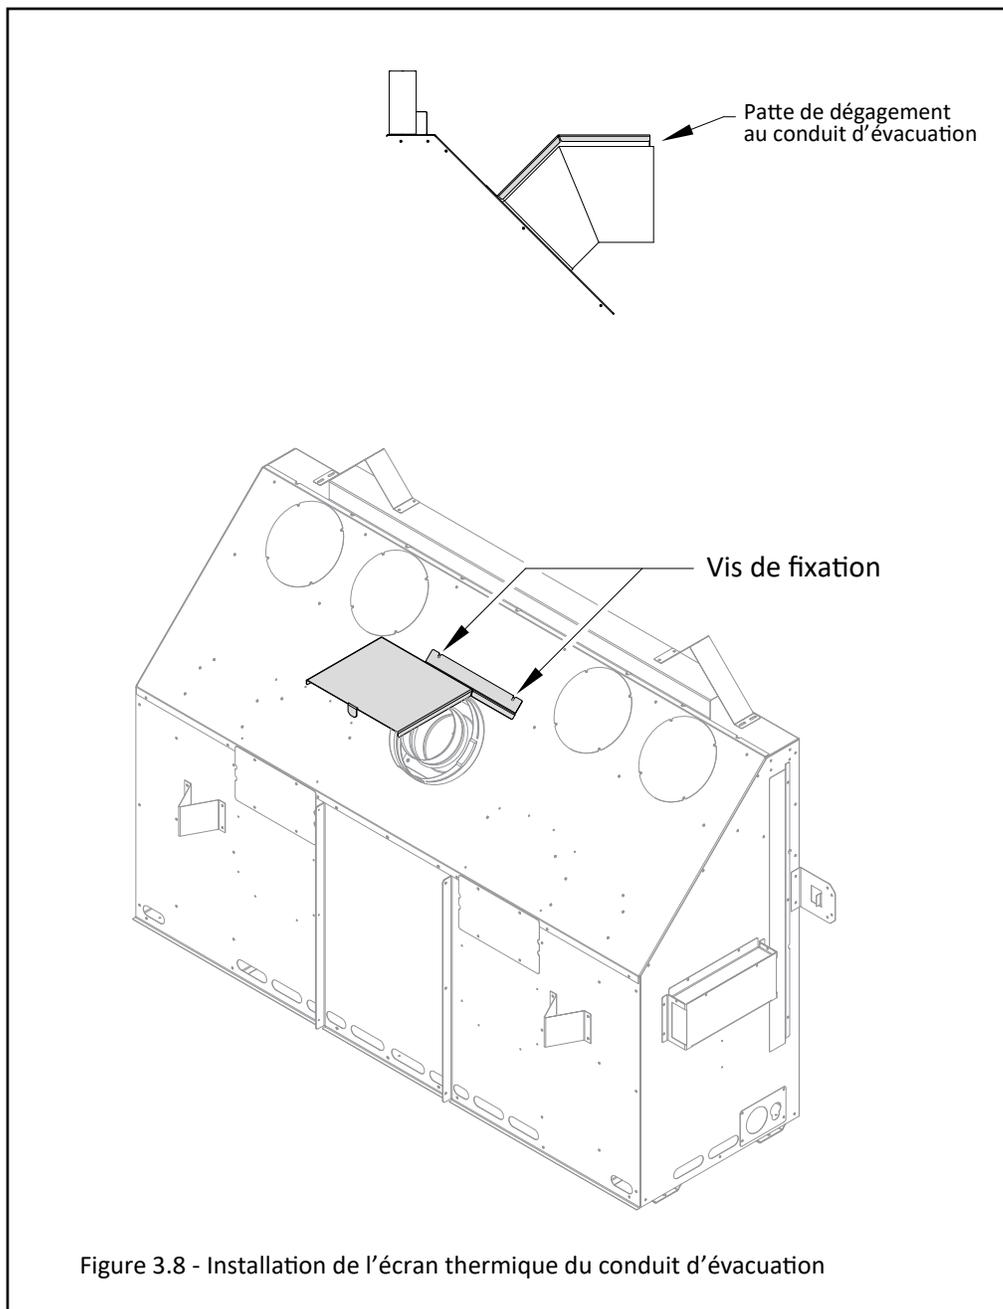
Installation de l'écran thermique du conduit d'évacuation
